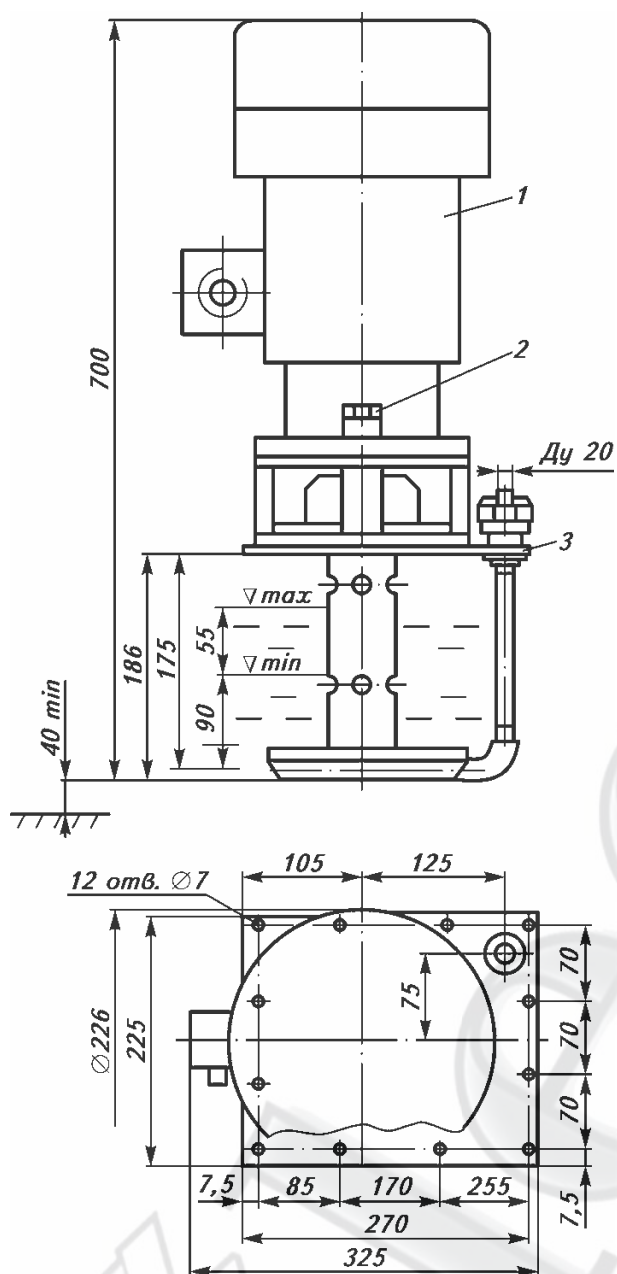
Общий вид, габаритные и установочные размеры электронасосного агрегата
